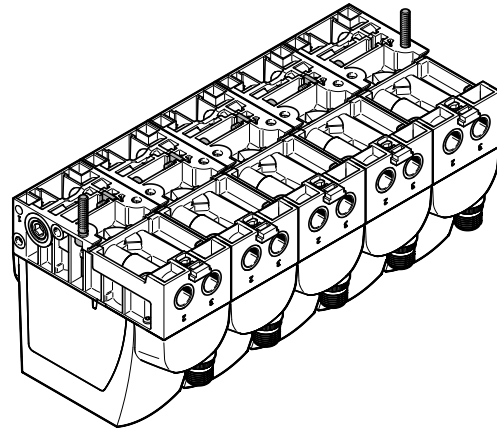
Befestigung verketteter Ventile mit seitlichen Schrauben M4
